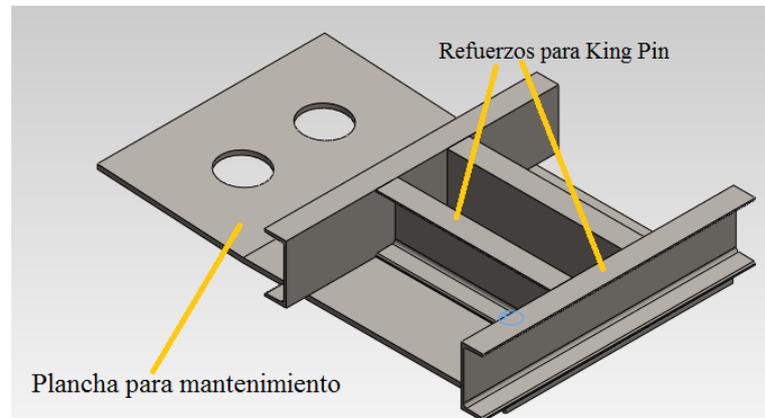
Conjunto plancha y refuerzos para king pin⁸⁰
